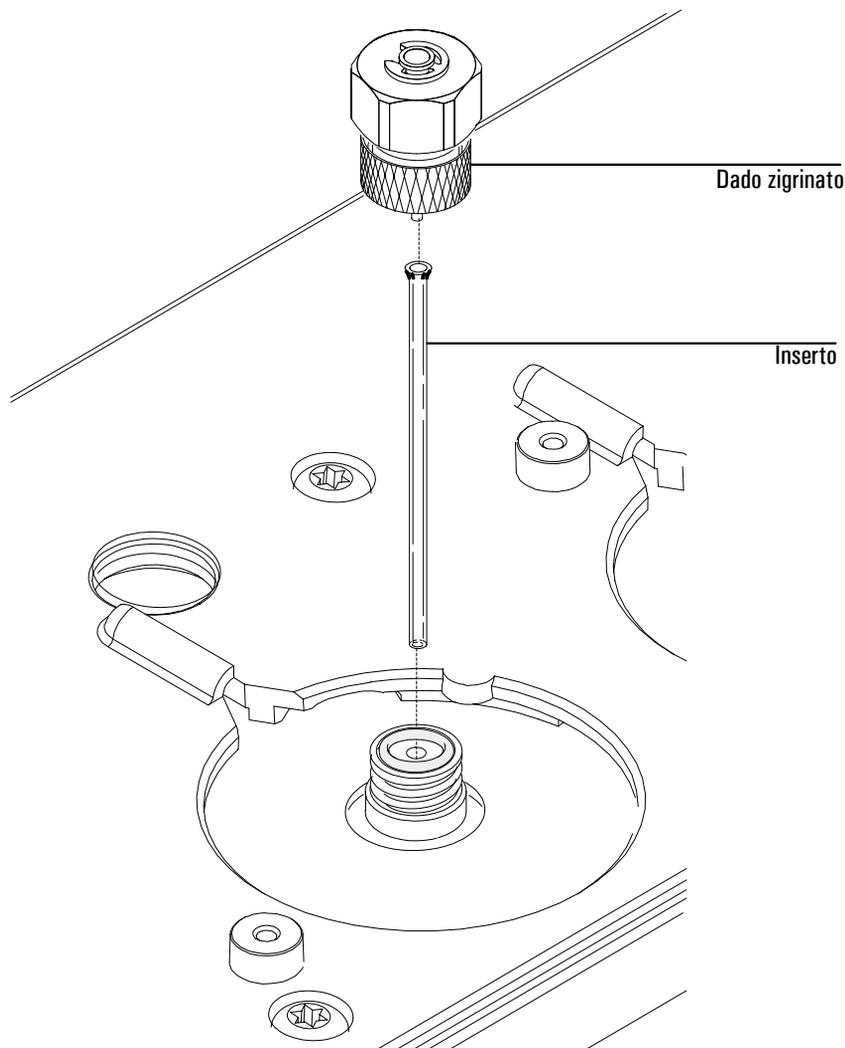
Installazione di un inserto di vetro in un iniettore per impaccate
